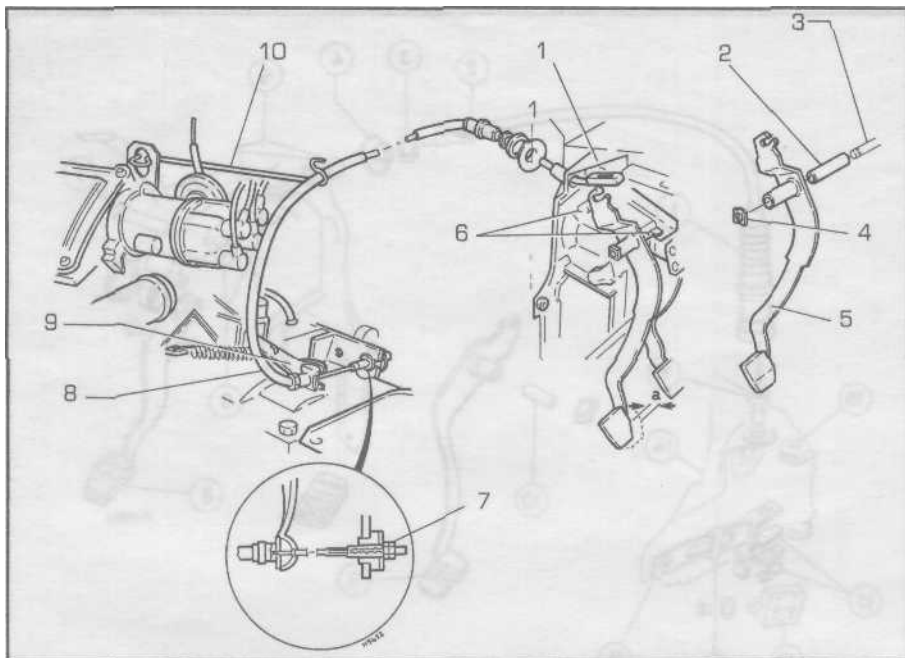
1, а. Детали педали и троса сцепления - коробка передач 084
